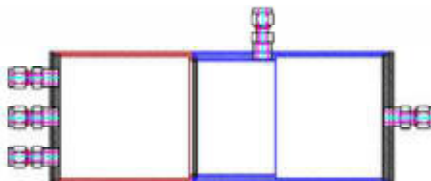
Чертеж камеры смешения для приготовления газовых смесей методом динамического смешения потоков
